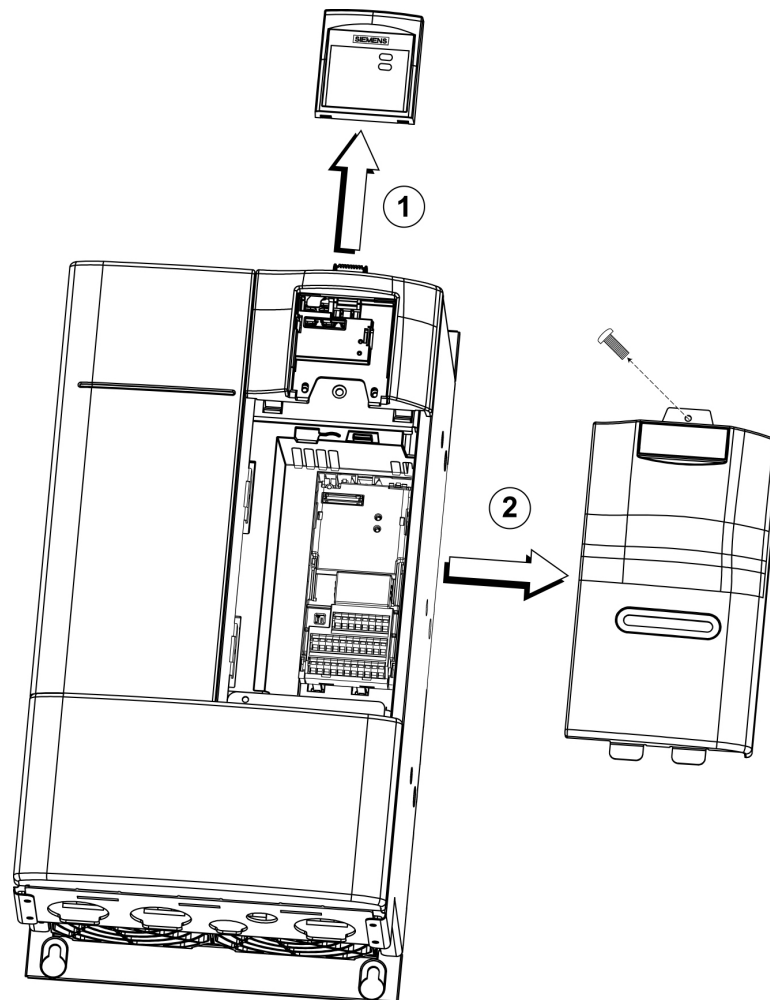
Demontage der Abdeckungen bei den Bauformen D, E, F
